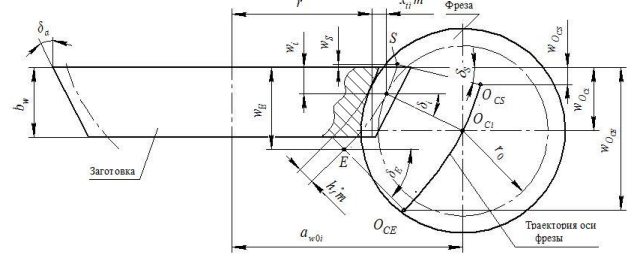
Схема станочного зацепления заготовки шестерни и фрезы
